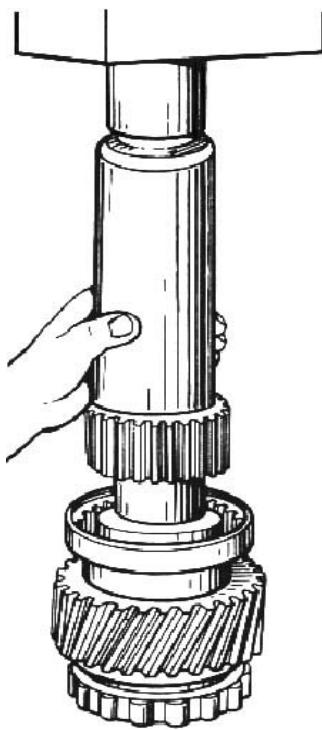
Напрессовка шлицевой втулки синхронизатора на промежуточный вал
